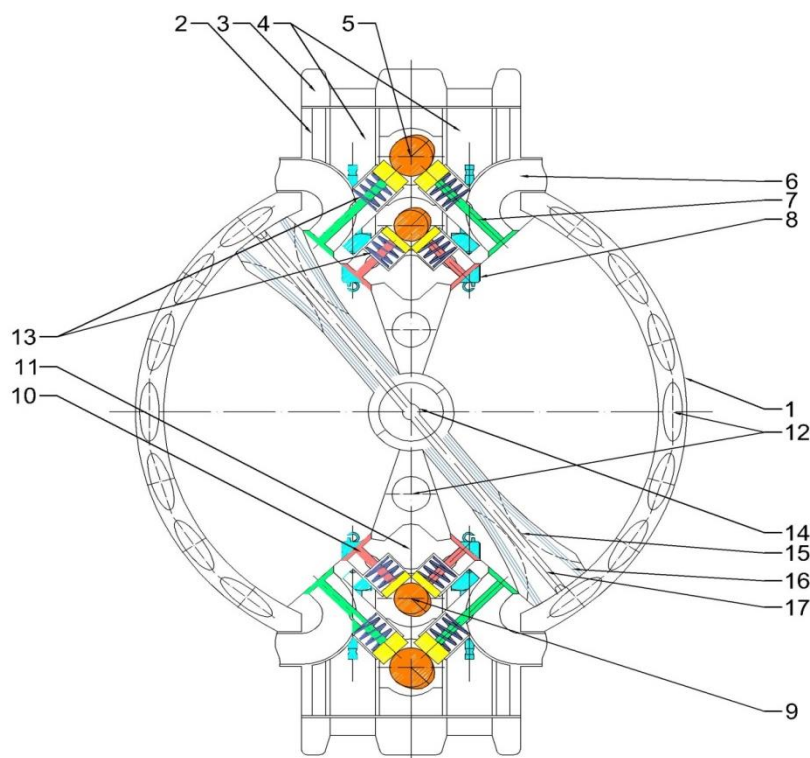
Конструктивная схема лопастного двигателя внутреннего сгорания: 1 – корпус двигателя; 2 – корпус газораспределительного механизма; 3 – крышка корпуса газораспределения; 4 – свечные колодцы; 5 – кулачек распределительного вала впускных клапанов; 6 – впускной канал топливо-воздушной смеси; 7 – впускной клапан; 8 – свеча зажигания; 9 – кулачек распределительного вала выпускных клапанов; 10 – выпускной клапан; 11 – выпускной канал отработавших газов; 12 – технологические полости охлаждающей системы; 13 – пружины клапанов; 14 – вал лопасти; 15 – лопасть; 16 – уплотнительные элементы; 17 – масляный канал.
